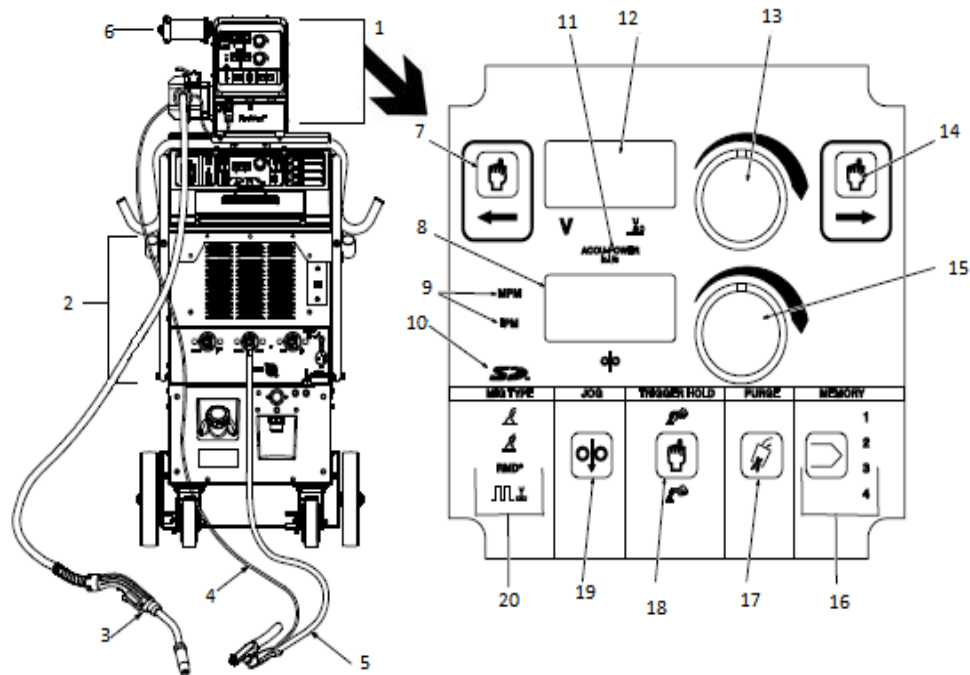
schéma du poste de soudage Miller PipeWorx 400 (380/400Volt).
